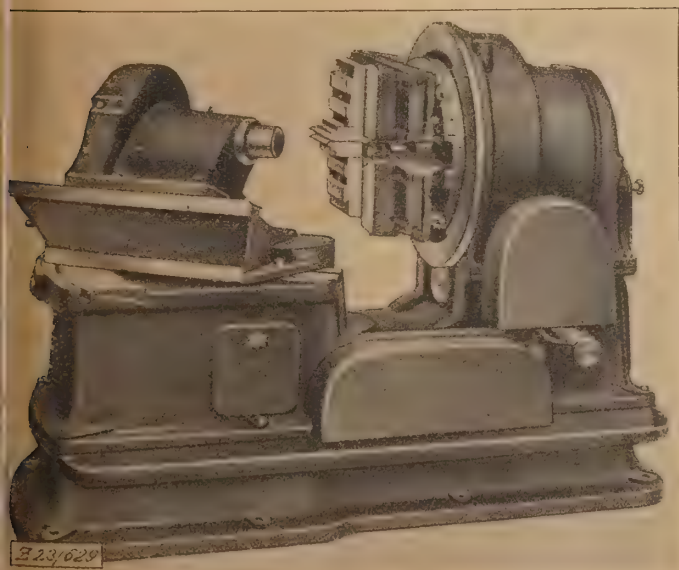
Selbsttätige Kegelradhobelmachine, Bauart Dr. Ing. Barth.
